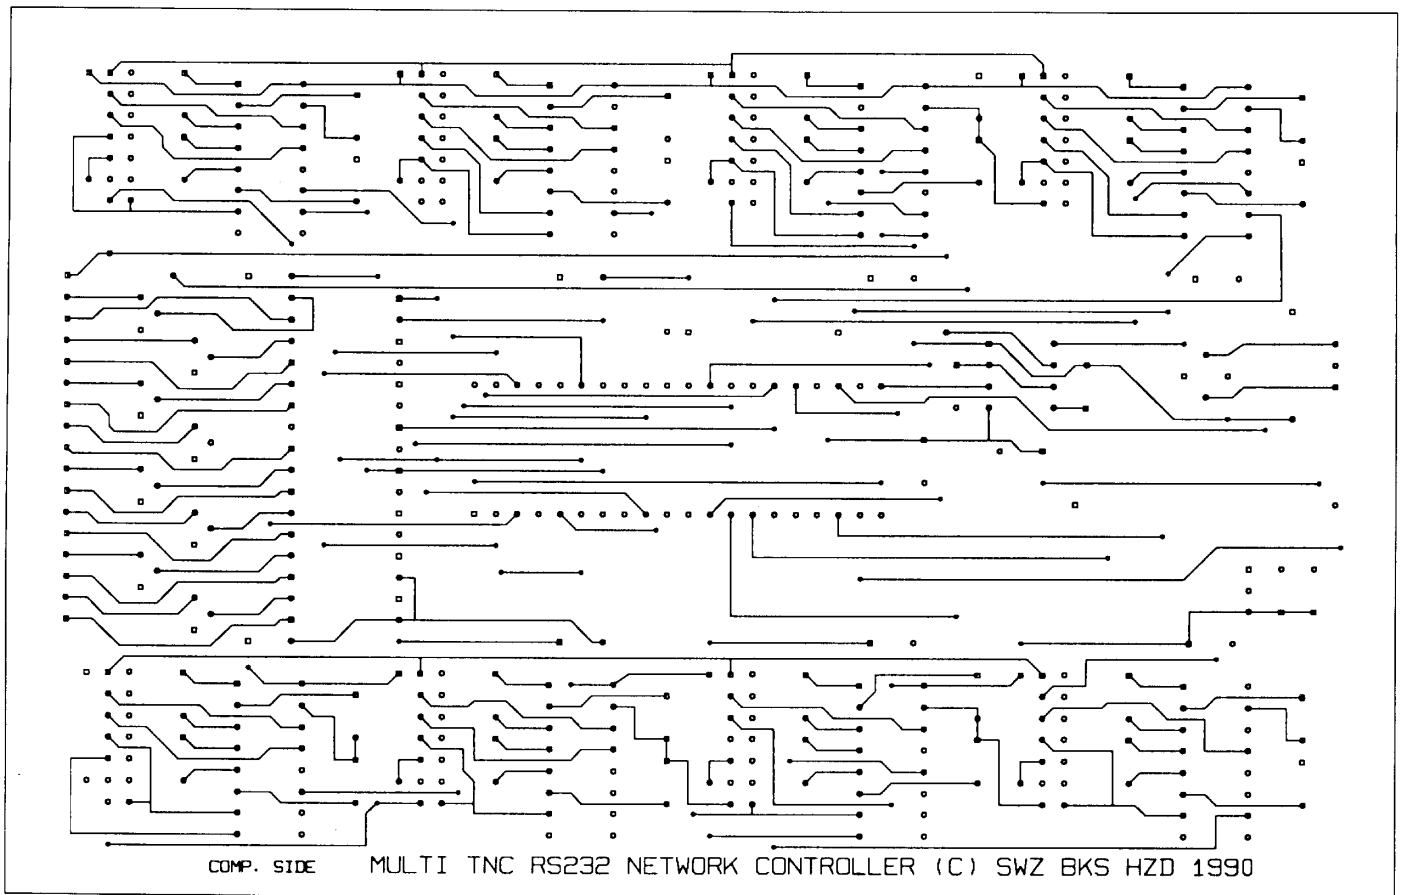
PCB layout knooppuntregelaar, componenten zijde.
